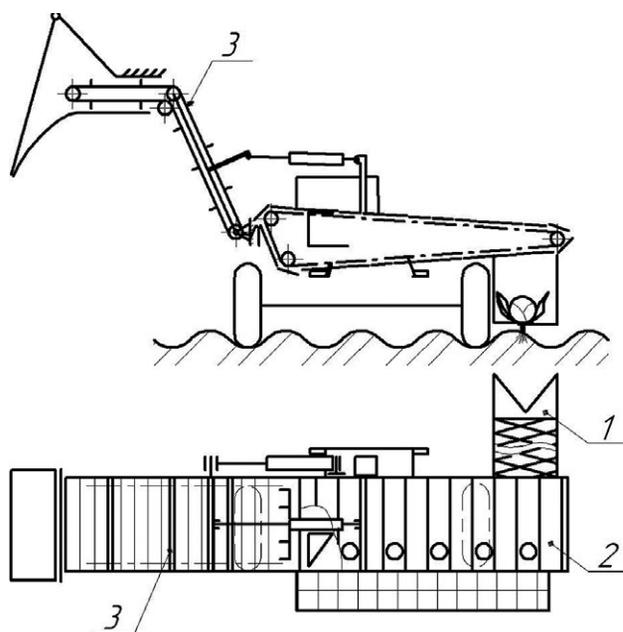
Схема компоновки многовариантного капустоуборочного комбайна с элеватором: 1 — режущий аппарат; 2 — стол доработки с транспортер-обрезчиком; 3 — элеватор.
